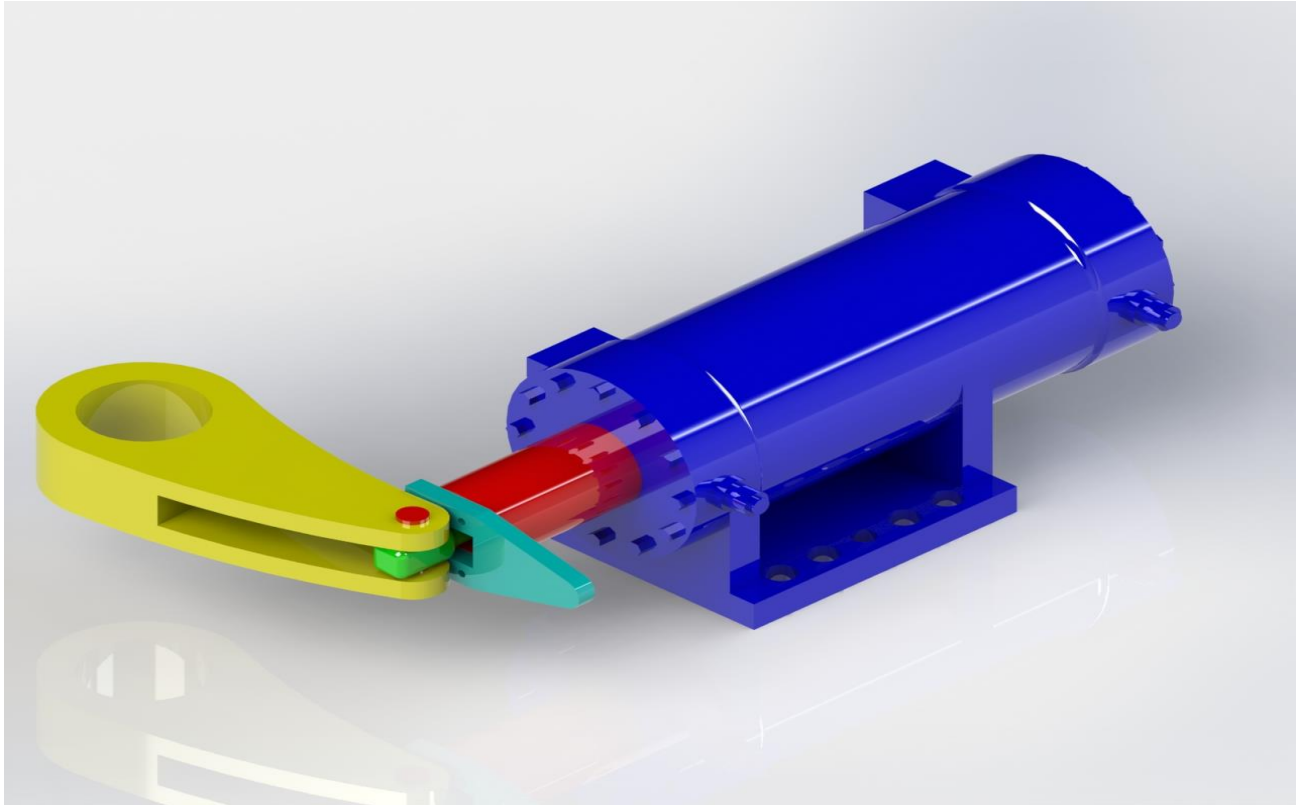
Cilindro actuador de doble efecto vista frontal izquierda.
